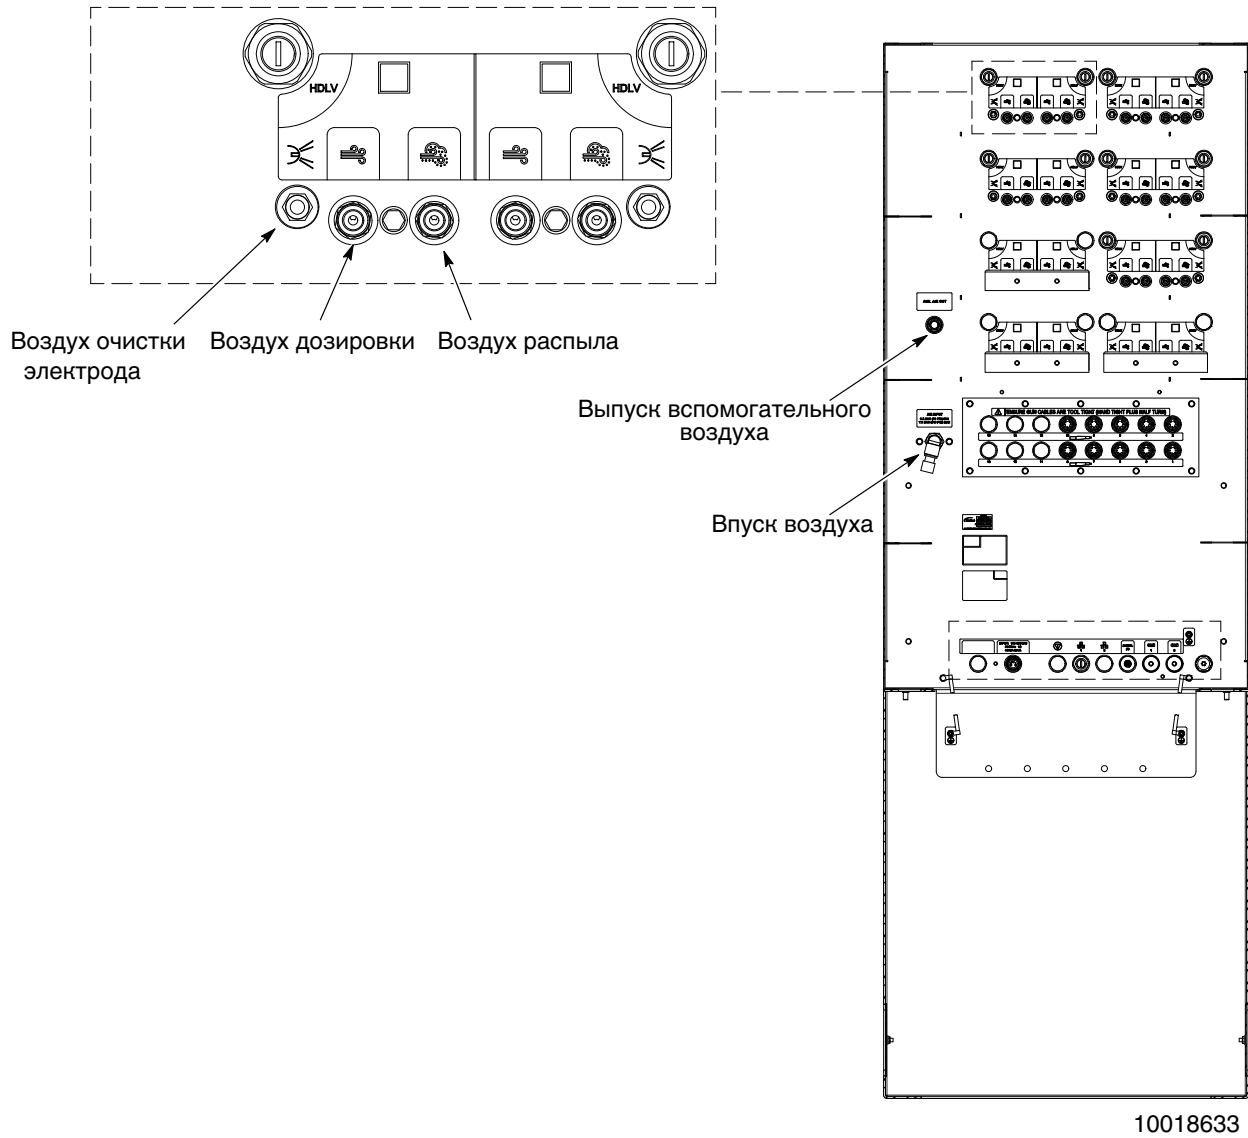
Пневматические соединители с задней стороны (крышка снята)
